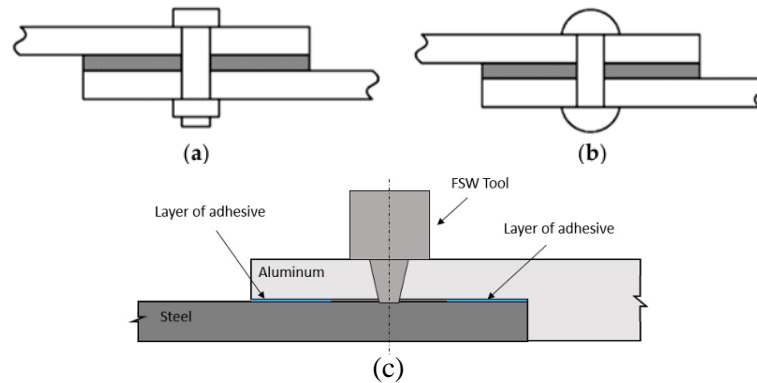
Différentes techniques d'assemblage hybride (a) un assemblage boulonné-collé, (b) un assemblage riveté-collé, (c) Soudage par points et collage .[27]
